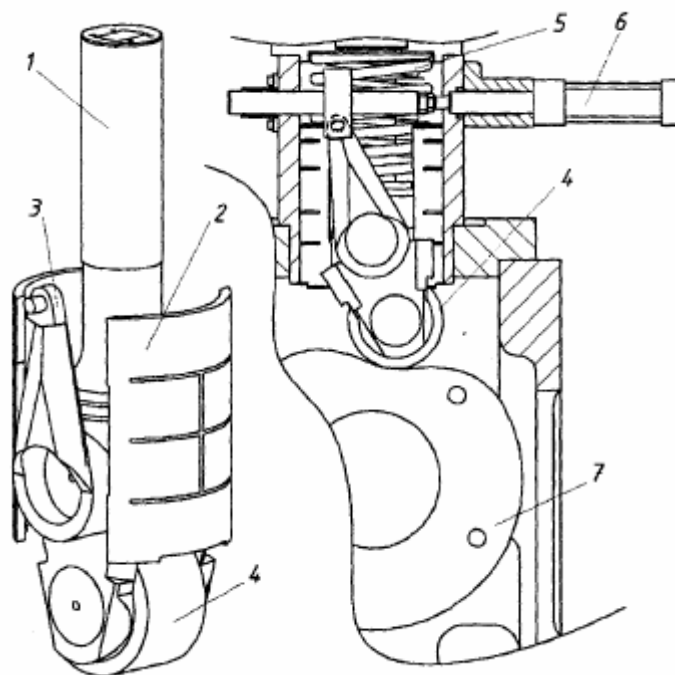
Штовхальник з механізмом реверсу дизеля серії МС фірми MAN: 1 - шток штовхальника; 2 - направляюча; 3 - важіль перекладання ролика; 4 - ролик штовхальника; 5 - поворотні пружини; 6 - пневматичний циліндр включення реверсу; 7 - кулачок приводу ТНВД.
